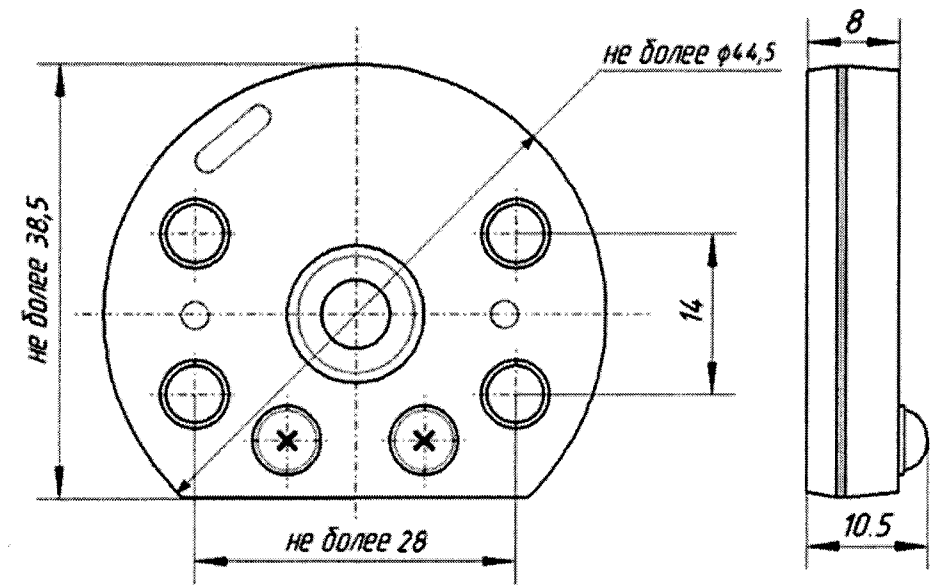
Корпус Т для установки внутри клеммной головки ПП. Степень защиты IP20.
